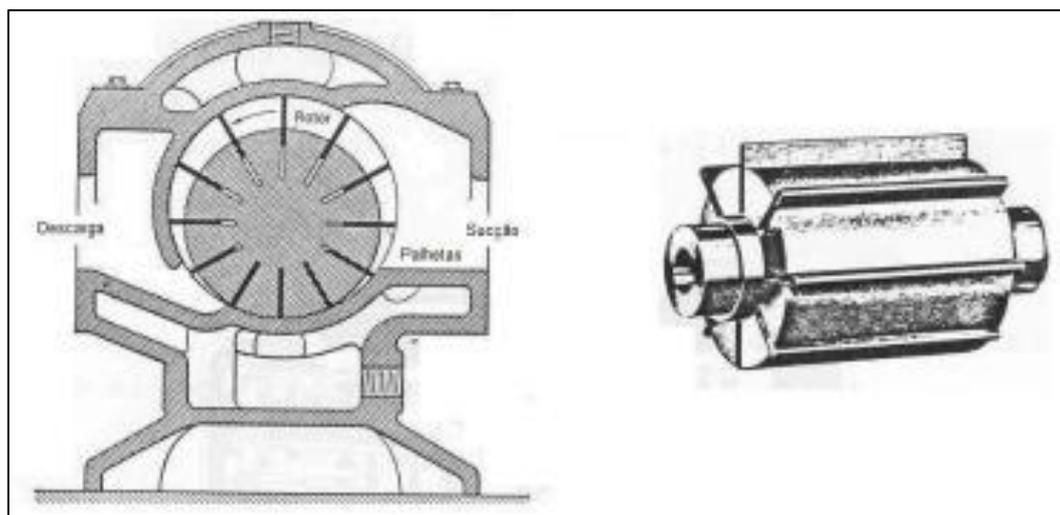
Detalhe de um compressor rotativo de palhetas.
